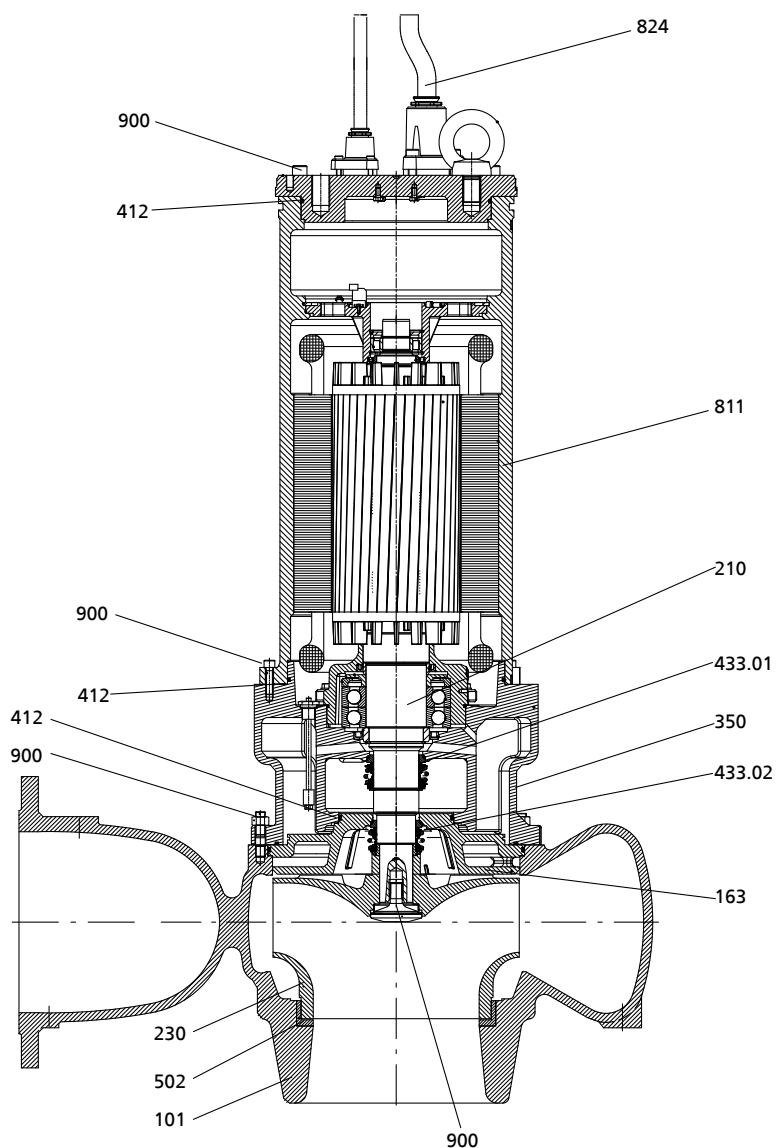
Сборочный чертеж, пример: Amarex KRT K 150-401 / 130 4 XNG-S без рубашки охлаждения
